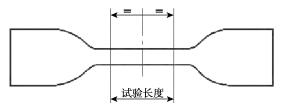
标准哑铃状拉伸试样(试样长度为(20.0±0.5) mm) Fig.2 tandard dumbbell-shaped test specimen (sample length: (20.0±0.5) mm)
